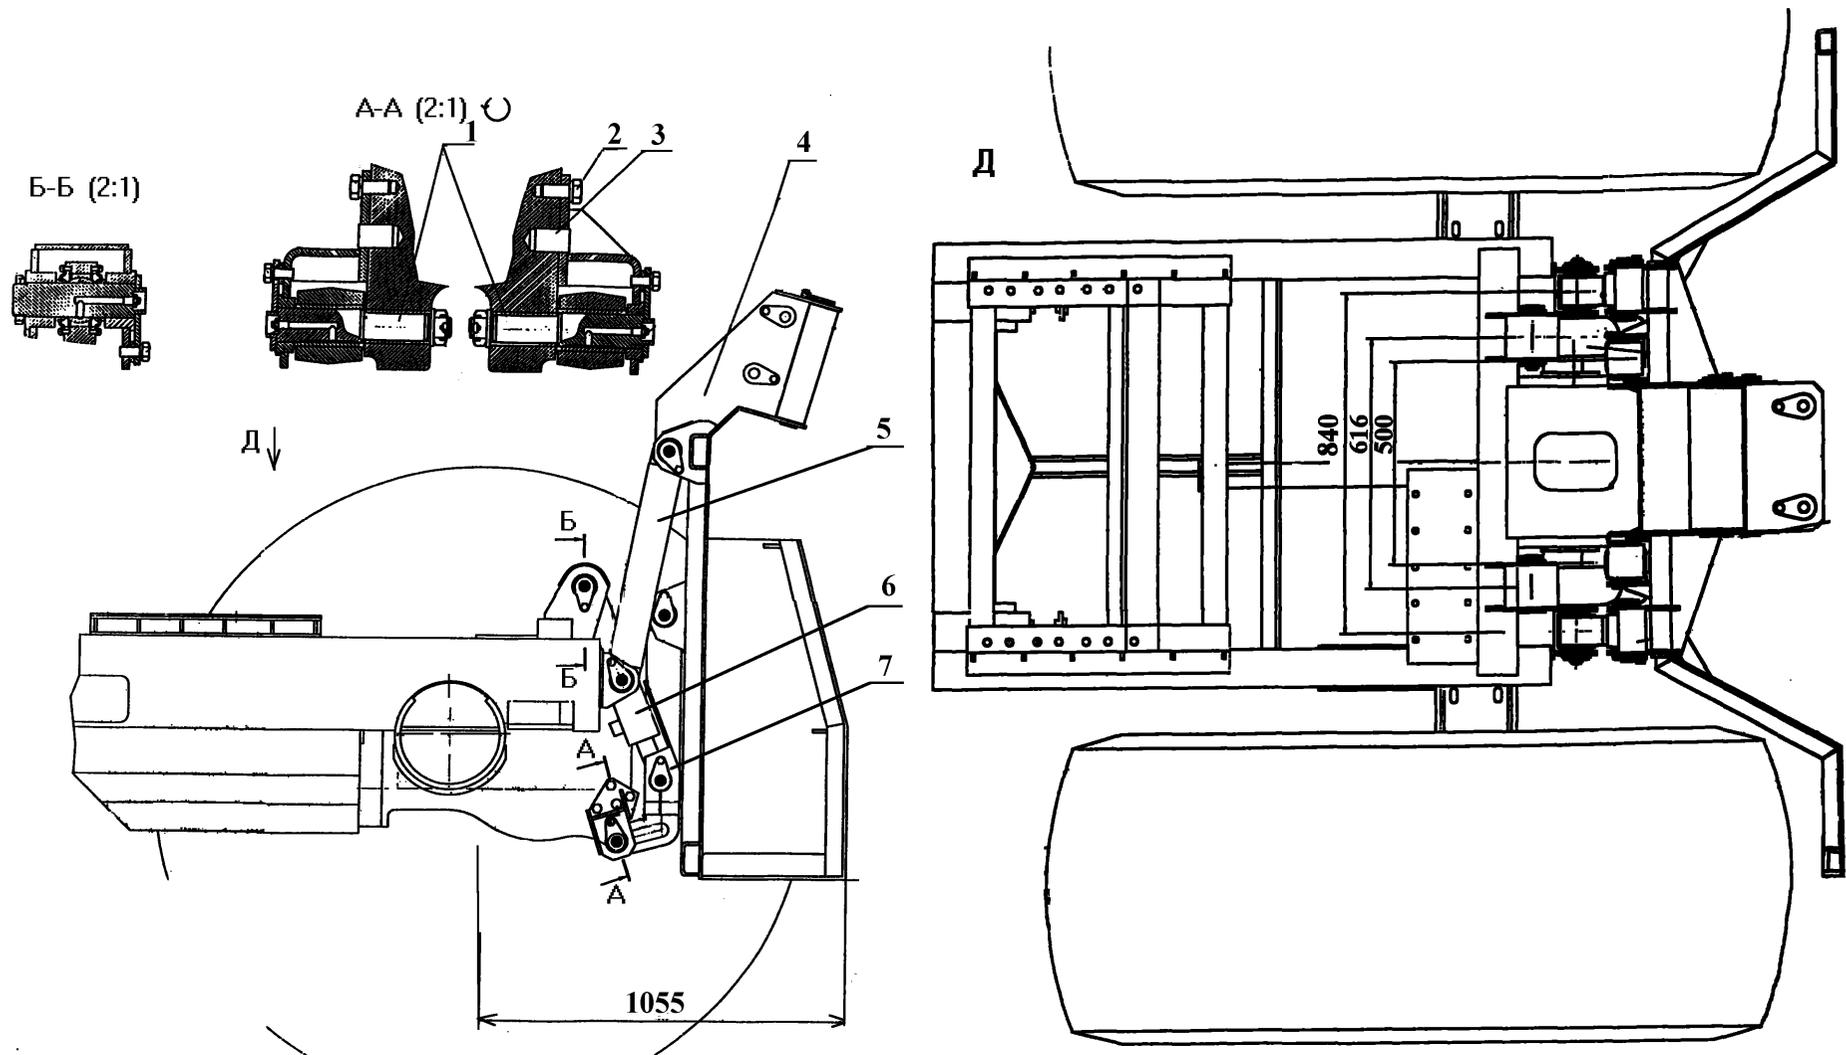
Схема установки щита трелевочной машины МЛ-126: 1 – ось; 2 – болт; 3 – штифт; 4 – щит защитно-опорный; 5 – тяга; 6 – гидроцилиндр; 7 – тяга
